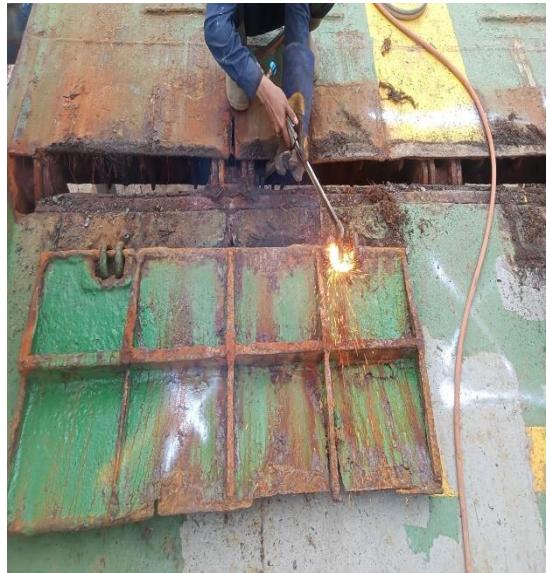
Pengelasan Pondasi Crane Kapal Geotin New 1.
